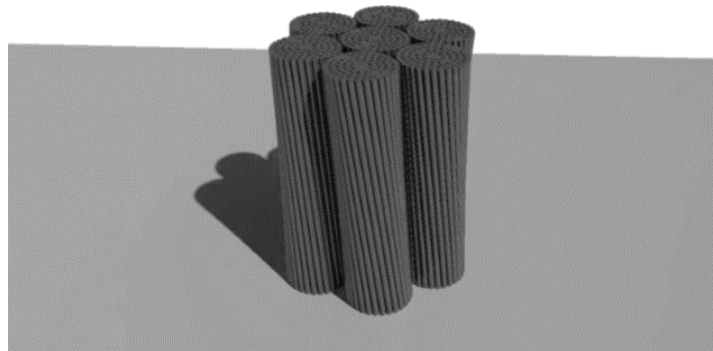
Structural wire rope (Martins, 2009).
